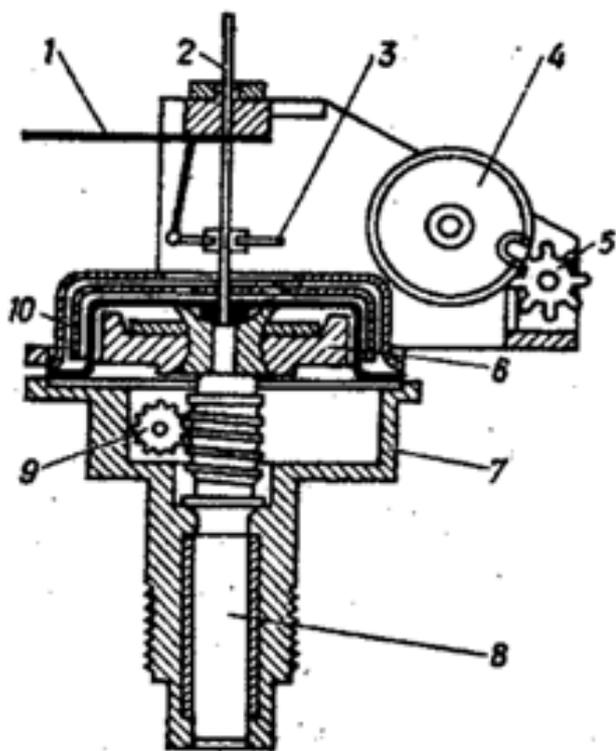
Механизм спидометра: 1 - регулировочная пластина; 2 - ось стрелки; 3 - волосок; 4 - барабанчик счетного узла; 5 - трибки; 6 - магнит; 7 - корпус; 8 - валик привода спидометра ведущий; 9 - валик ведомый; 10 - катушка
